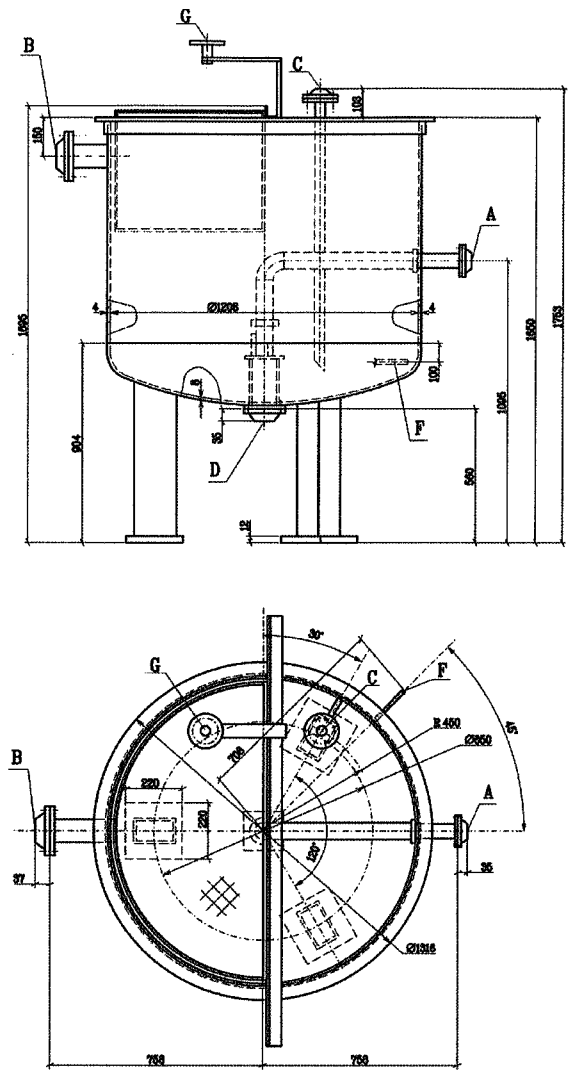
Габаритный чертеж мешалки фосфата QCT10AM001
